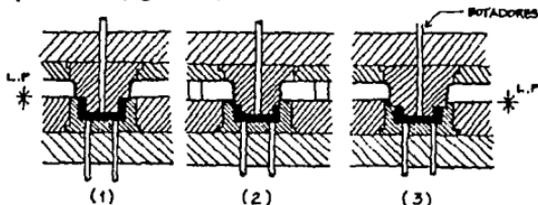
Tipos de moldes para Compresión: (1) Molde tipo Flash (2) Molde positivo (3) Molde semipositivo
